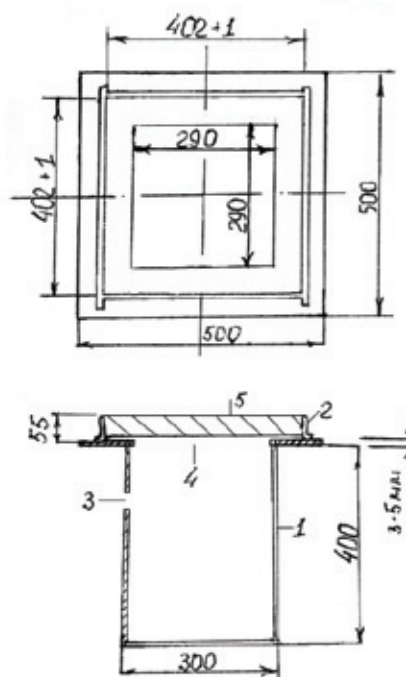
Устройство для съемки пятна контакта: 1 — металлический корпус для размещения линейной камеры; 2 — ограничители для бронестекла; 3 — отверстие для проводов; 4 — отверстие для крепления линейной камеры; 5 — бронестекло
